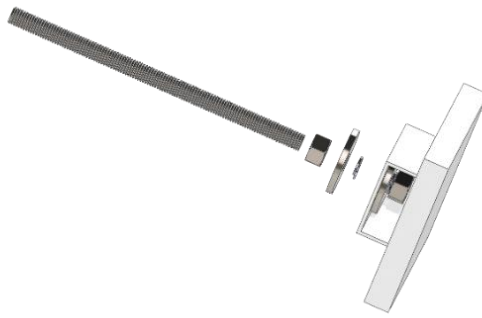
Montagem do refletor do sensor laser no suporte de fixação.
